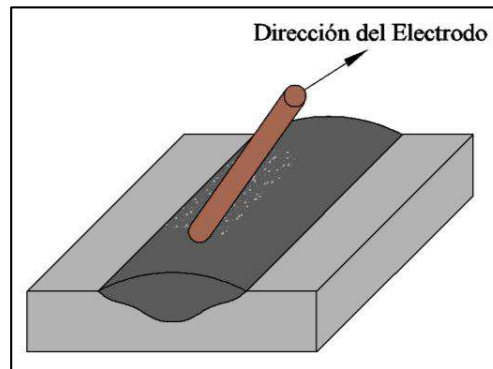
Escoria Atrapada en el Cordón de Soldadura.
